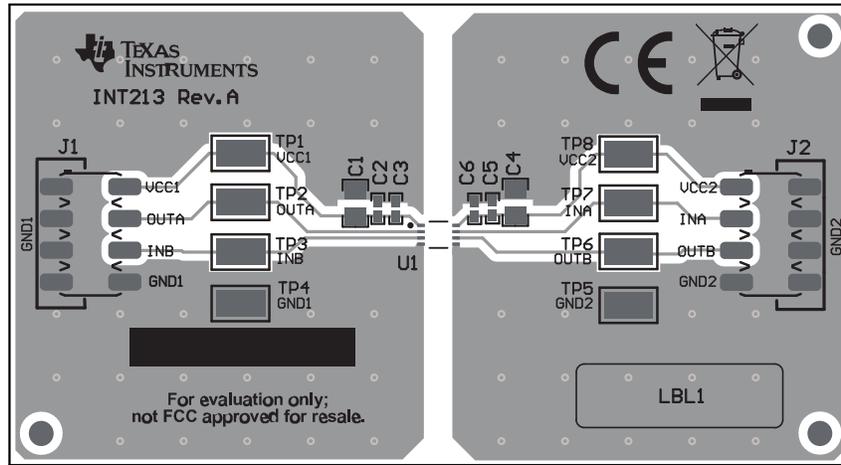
ISO6521REUEVM PCB 布局 - 复合顶视图
